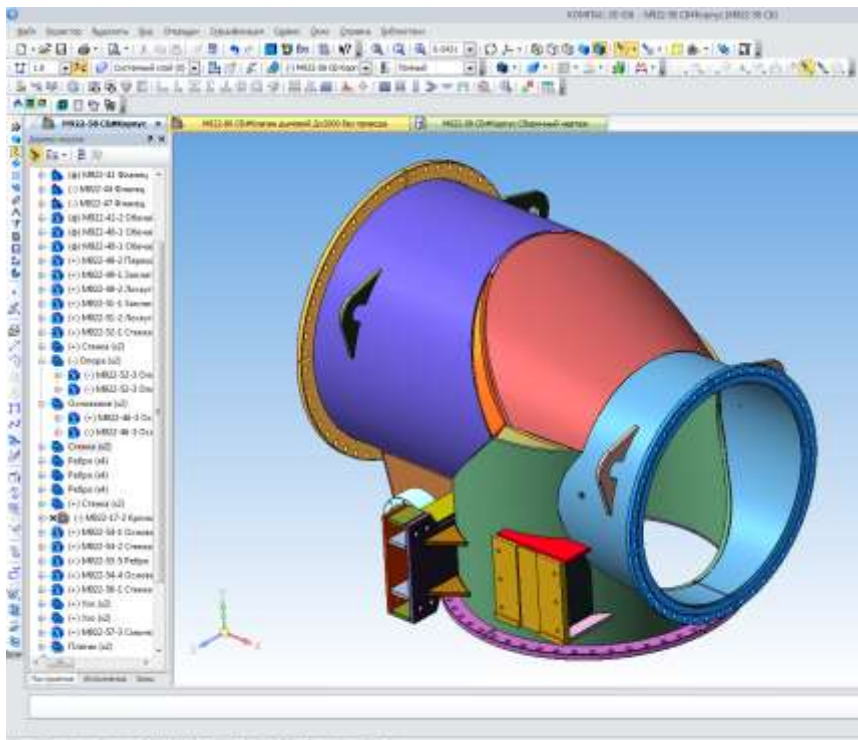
3D-модель корпуса дымового клапана Ду2000
